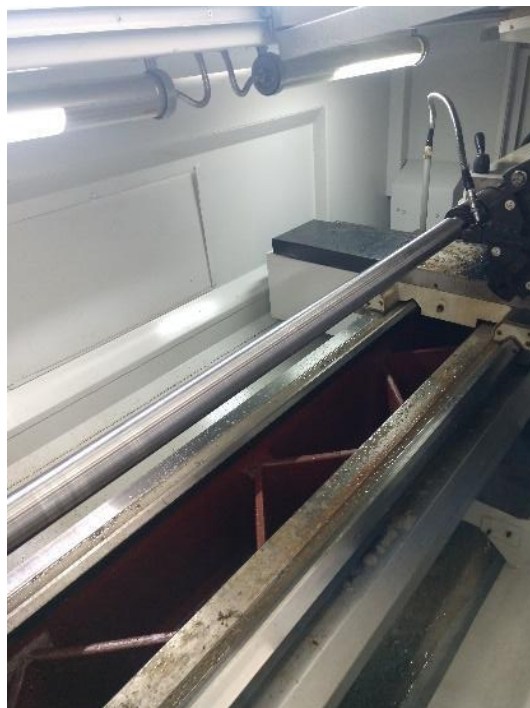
Torneado inicial de husillo para ajuste al barril (maquinado previo al de formación de alabes). Actividad realizada dentro de ITPA. Disminución de diámetro de 50 a 48.5 mm.
